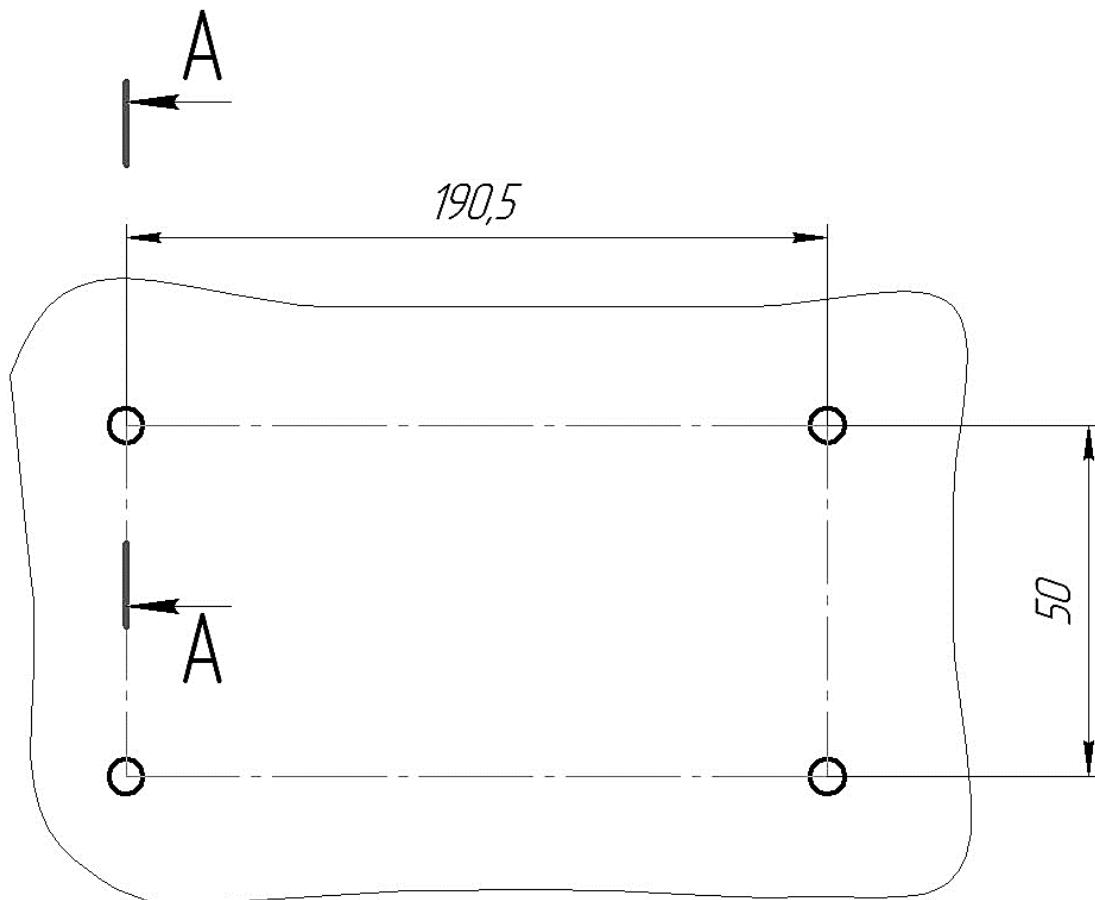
Разметка отверстий для крепления коробки распределительной КР-ПУИ-1
